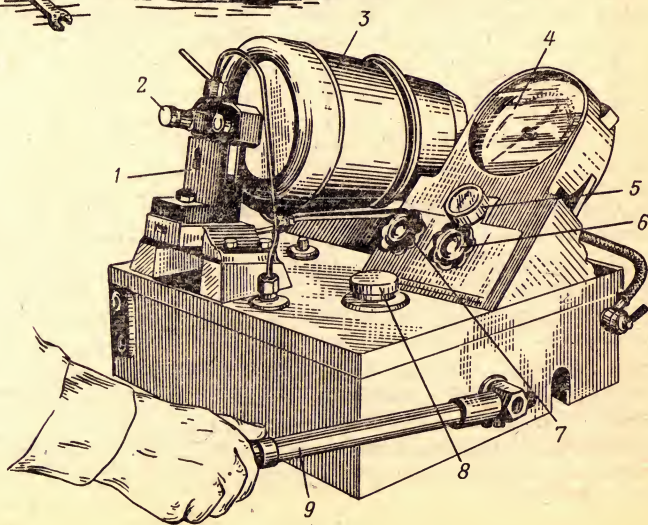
Прибор КИ-3333 для проверки и регулировки форсунок:
